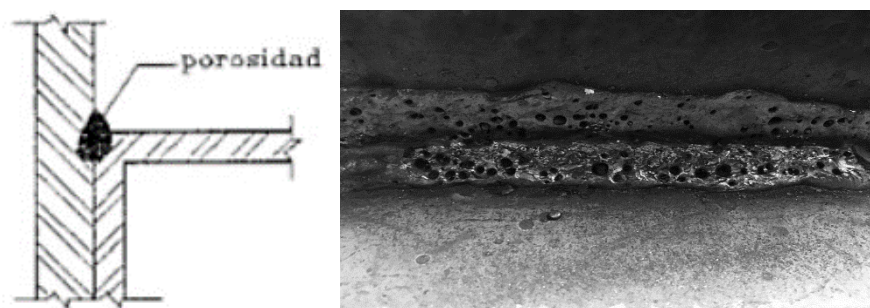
Detalle de falla en conexión soldada por porosidad
